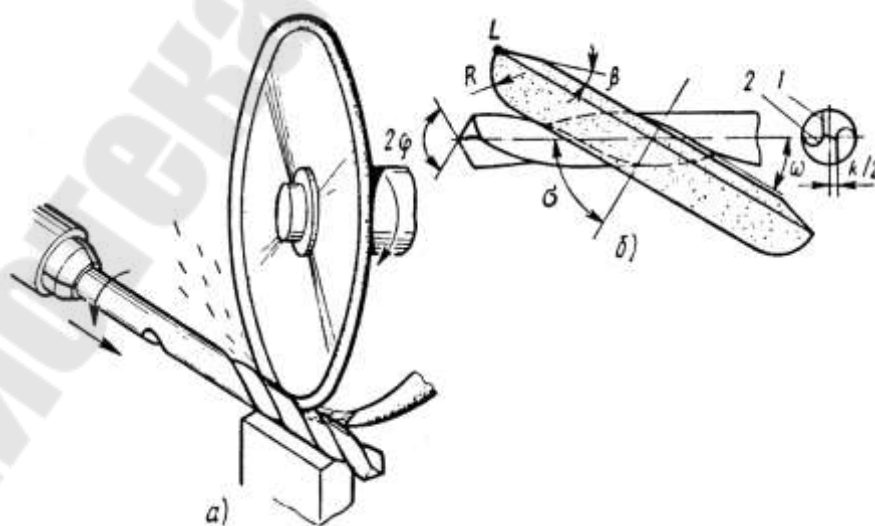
Расположение спирального сверла и абразивного инструмента при вышлифовке винтовых стружечных канавок: *a* – внешний вид; *б* – схема:
